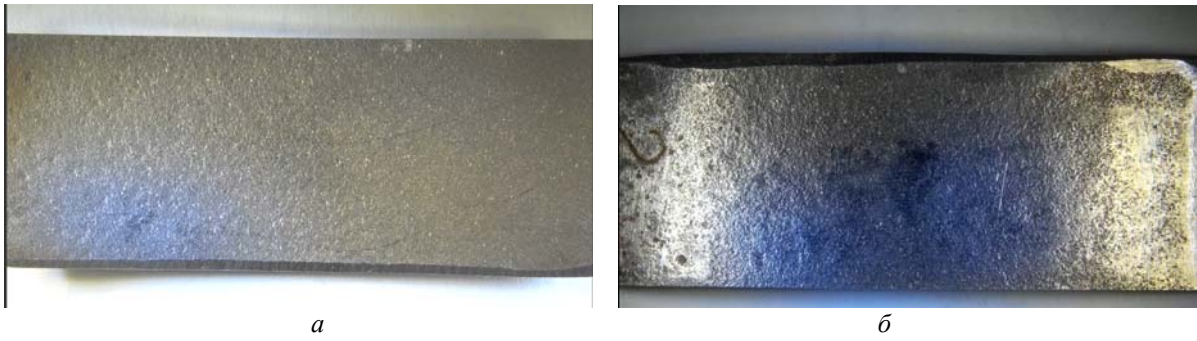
Съёмный литой образец – имитатор пера лопатки из стали 08X14H7МЛ:
